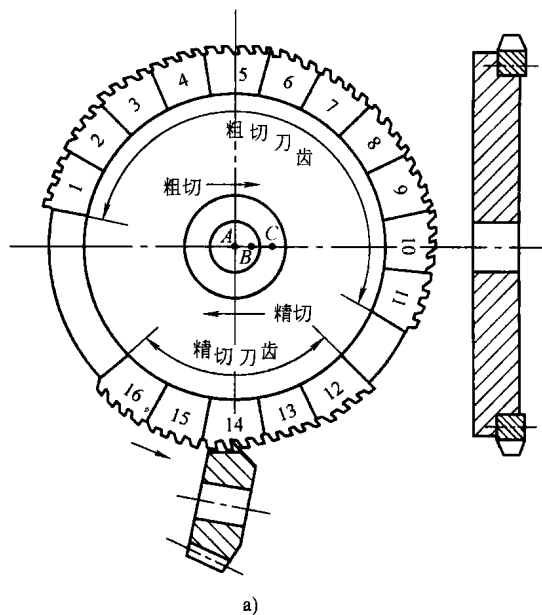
圆拉铣刀切直齿锥齿轮原理图
